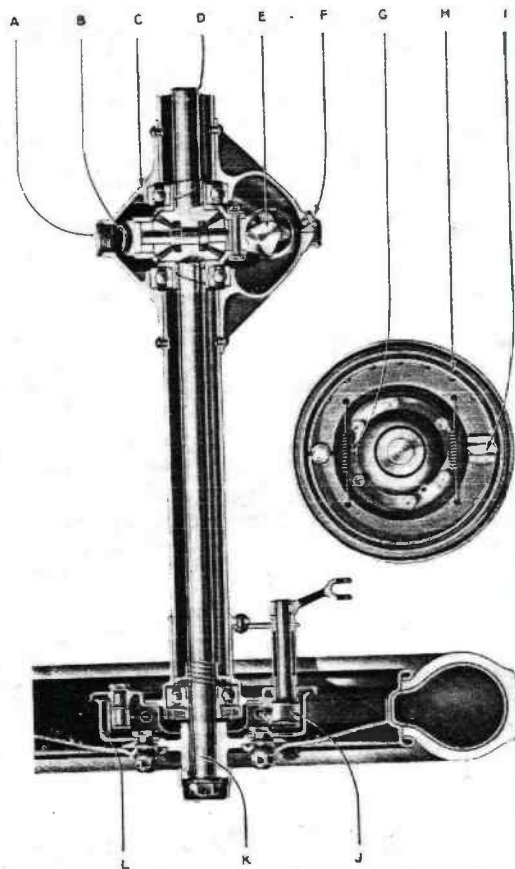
Coupe du pont arrière et vue d'un frein.
